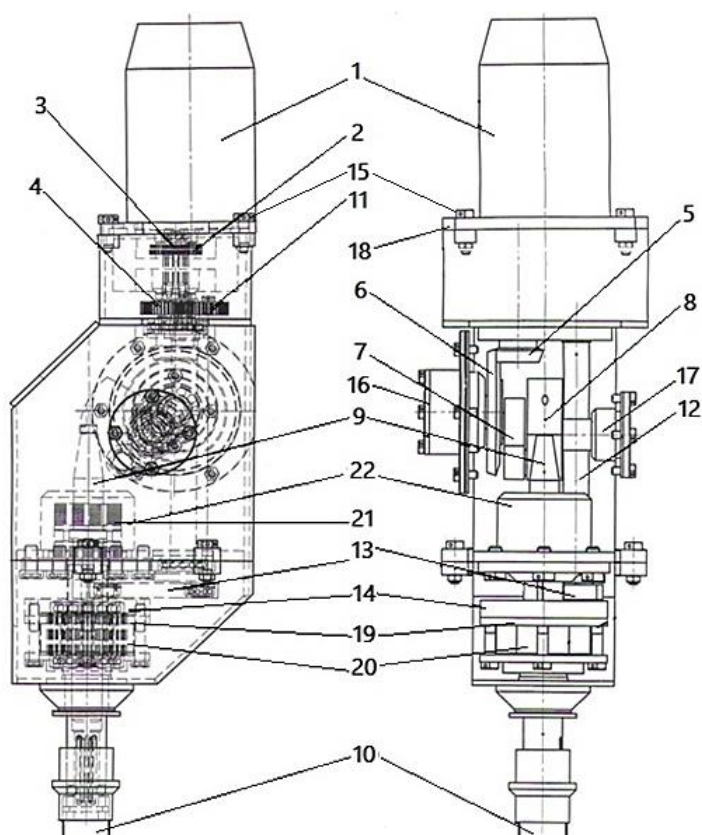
Принципиальная конструктивная схема опытного образца перфоратора с ударно-поворотным механизмом
